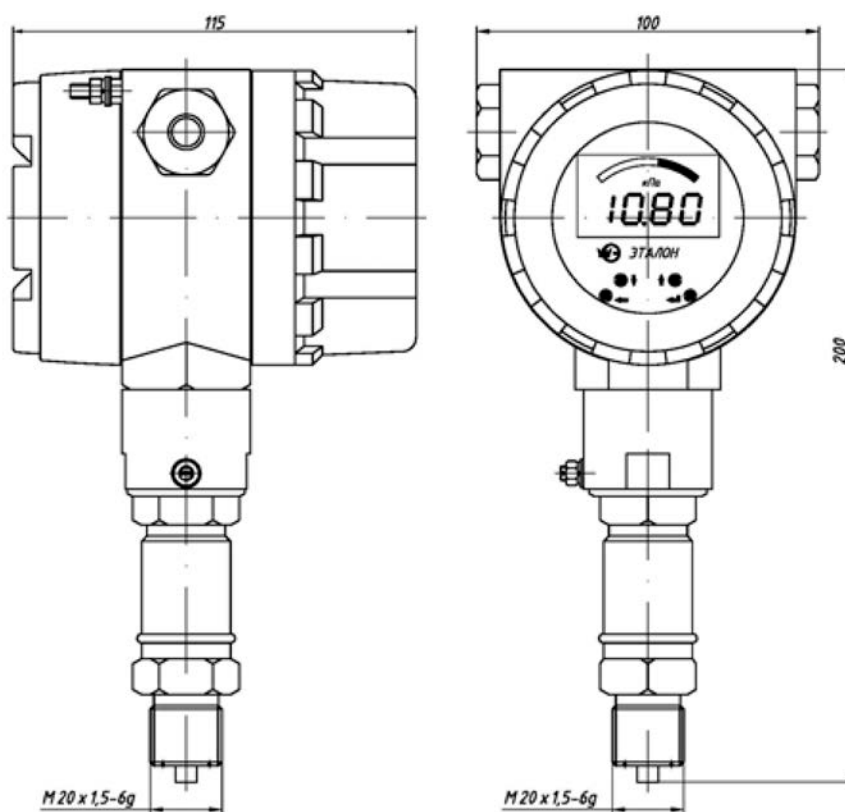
Габаритный чертеж датчиков абсолютного давления
